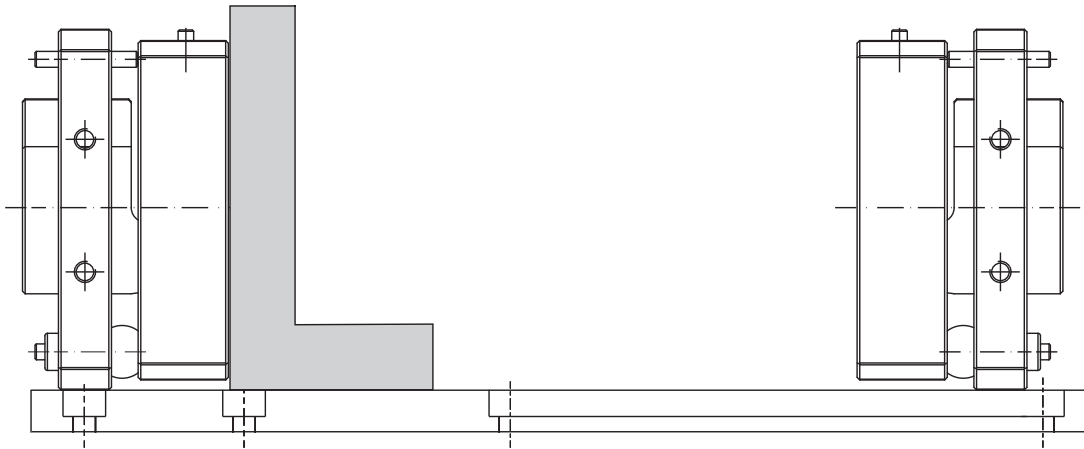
Seitenansicht Montageplatte und Montageadapter mit angelegtem Winkel
